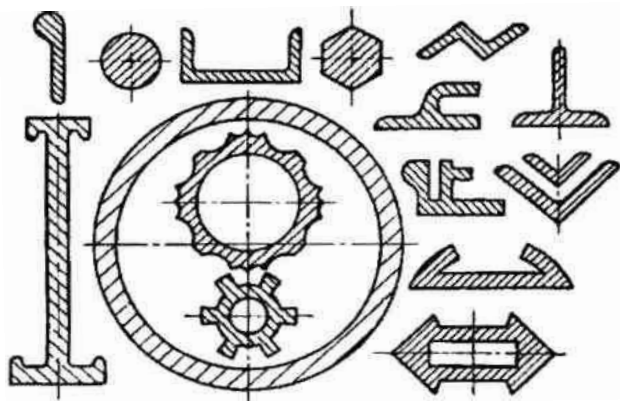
Поперечные сечения профилей изделий, изготовленных прессованием
